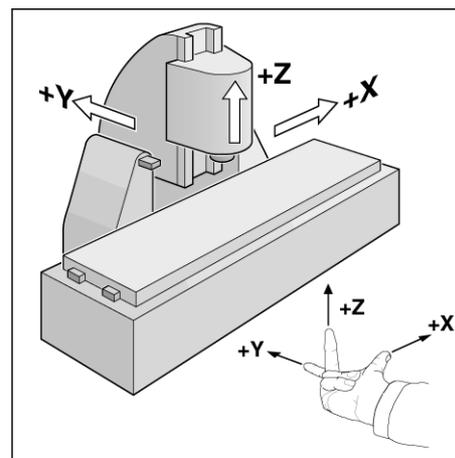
Désignation et sens des axes de la machine sur une fraiseuse
